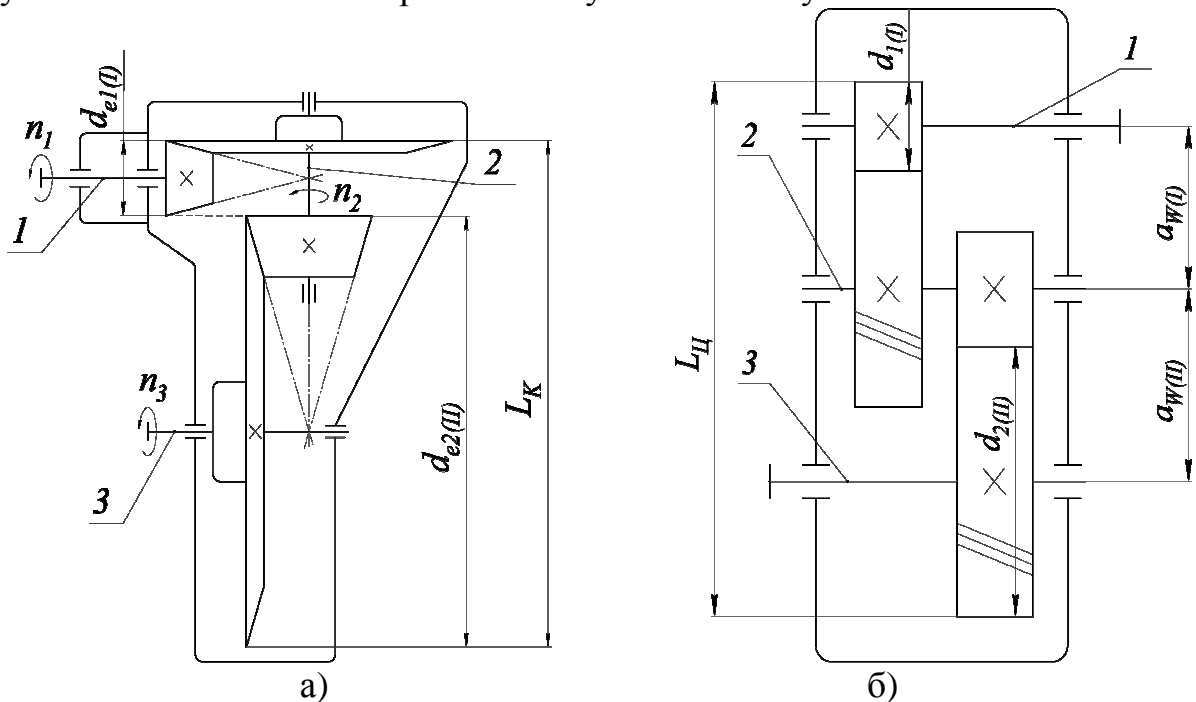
Кинематические схемы двухступенчатых редукторов К2 и Ц2
